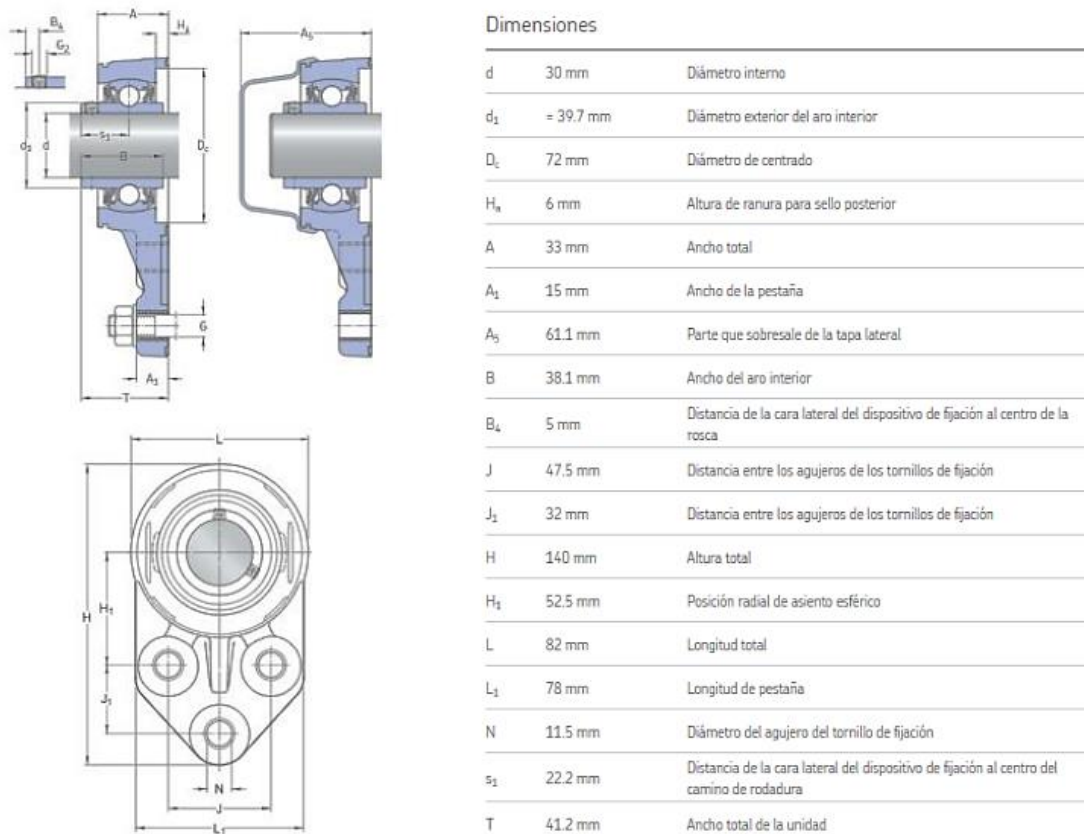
Dimensiones del rodamiento con pestaña F3BBC 30M-TPSS [34].
